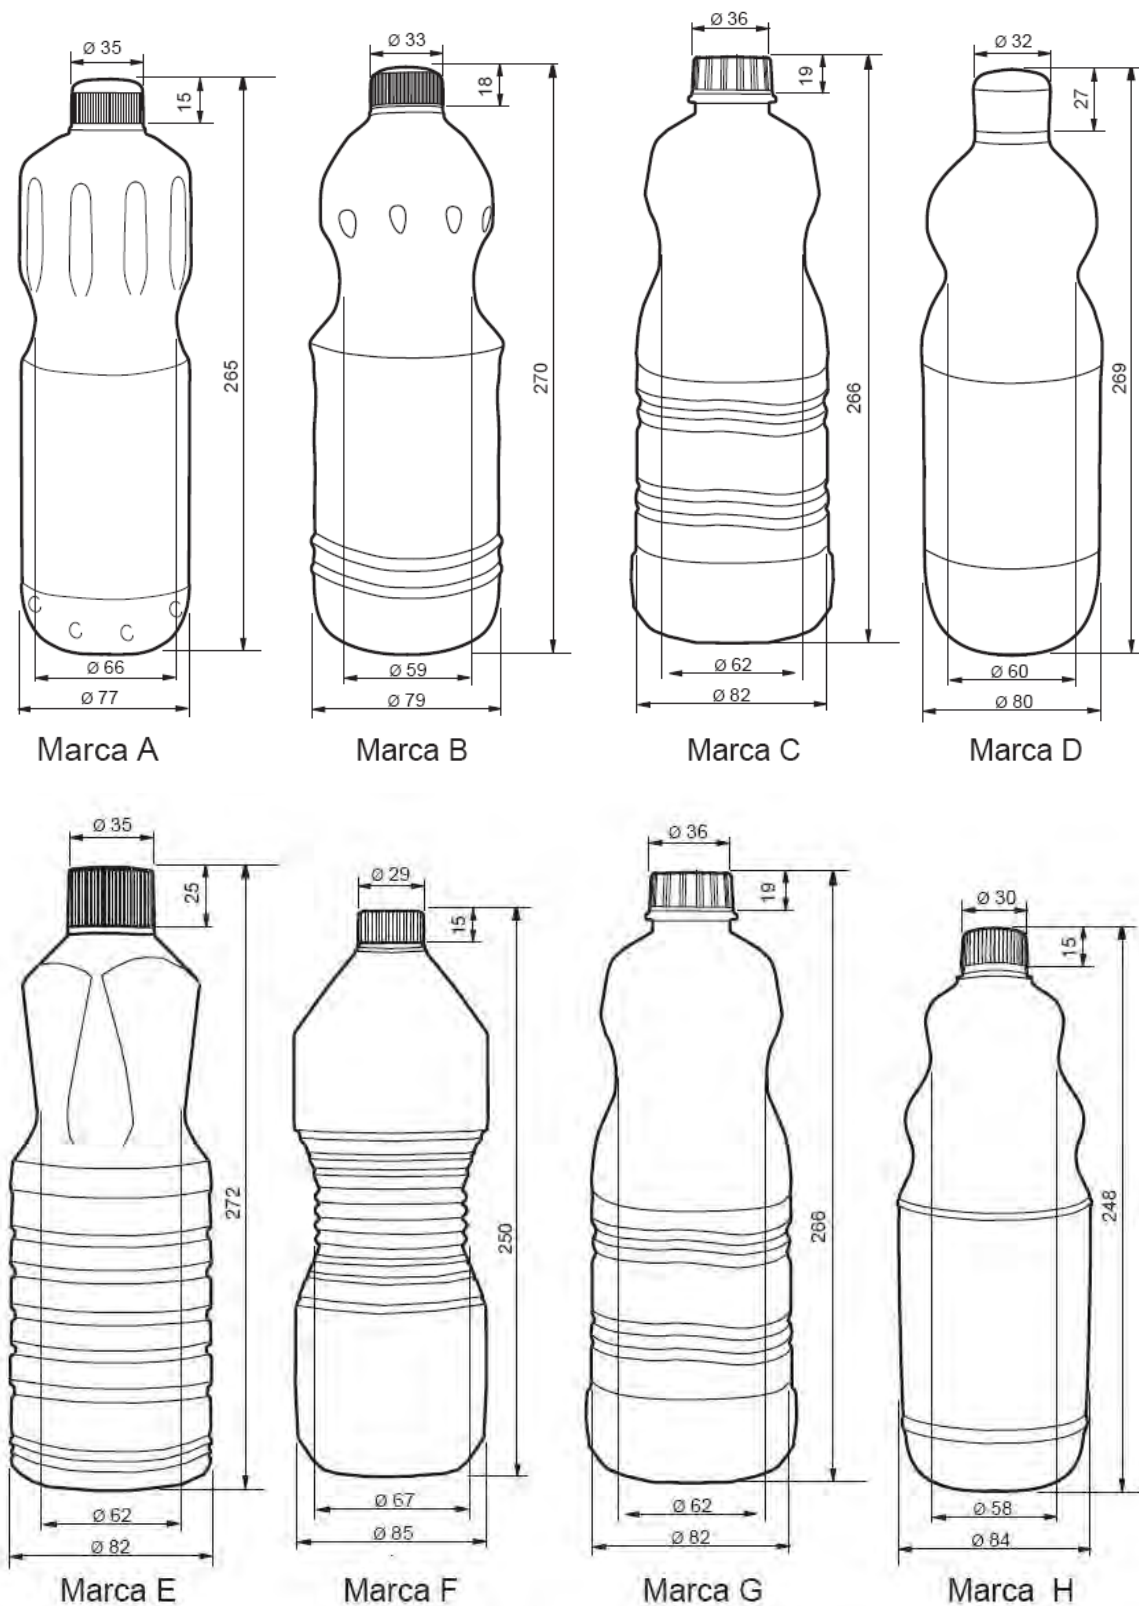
Dimensões das embalagens (Dimensões em milímetros)
